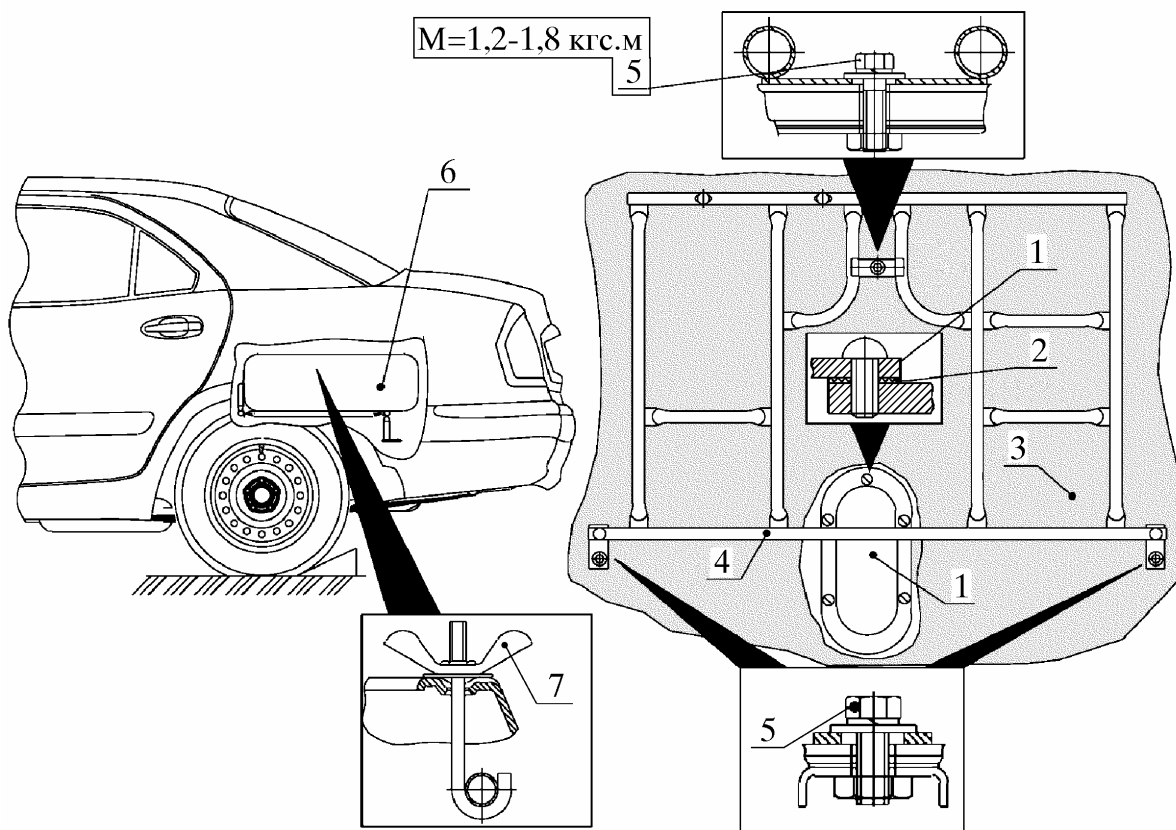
Установка крышки люка, держателя и запасного колеса:
